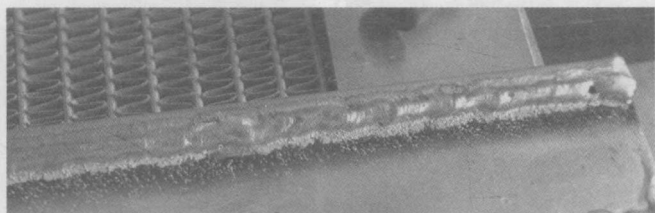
平对接焊缝引弧/收弧处的焊接缺陷 (一)
